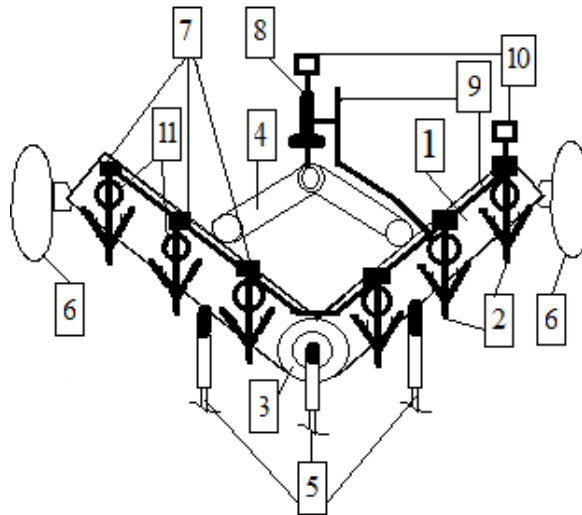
Схема адаптивного глубокорыхлителя (вид сверху)
